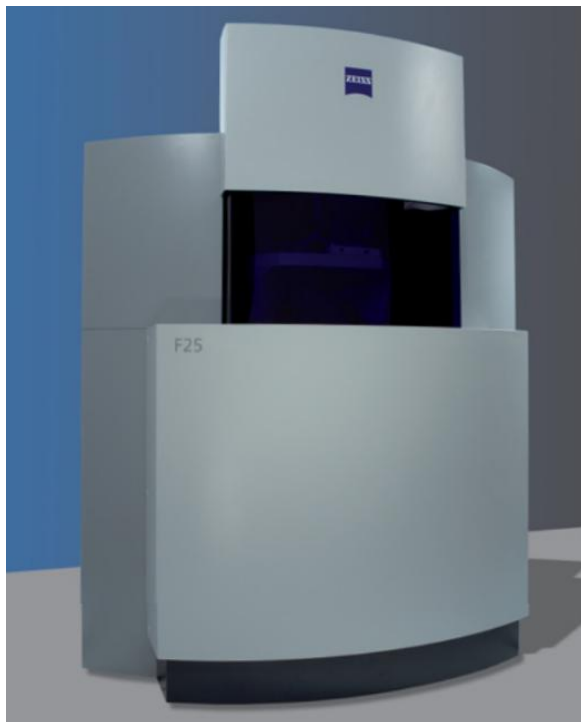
Souřadnicový měřicí stroj UNIVERSAL [5]
